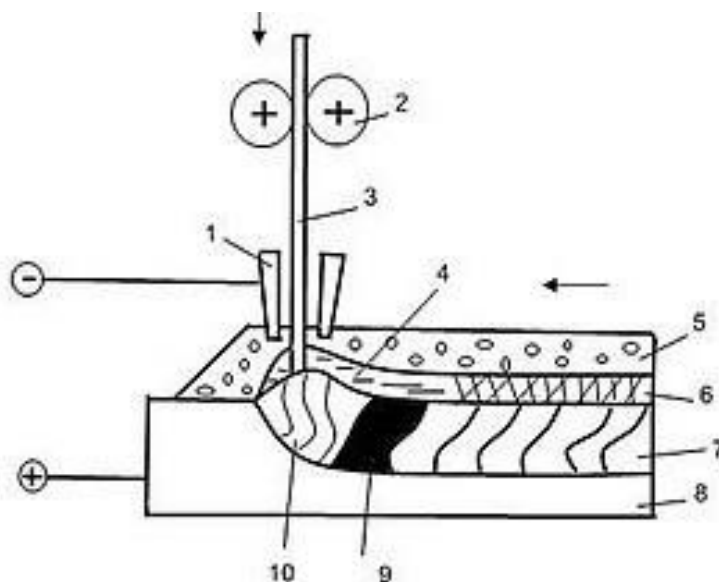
Схема дугового зварювання під флюсом. 1 – струмопровід, 2 – механізм переміщення дроту, 3 – дріт, 4 – рідкий шлак, 5 – флюс, 6 – шлакова кірка, 7 – зварний шов, 8 – основний метал заготовки, 9 – рідкий метал, 10 – електрична дуга
